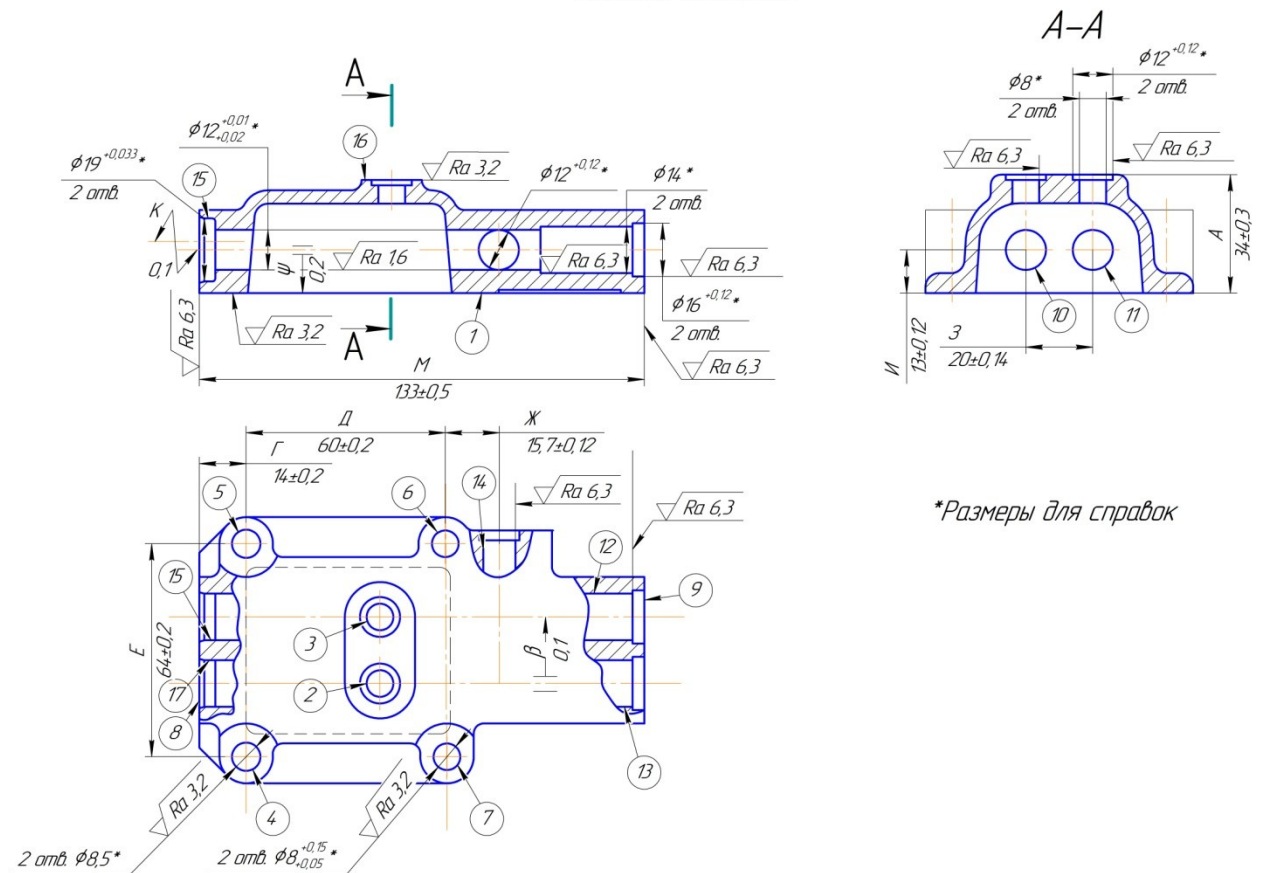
Эскиз крышки механизма переключения раздаточной коробки автомобиля
